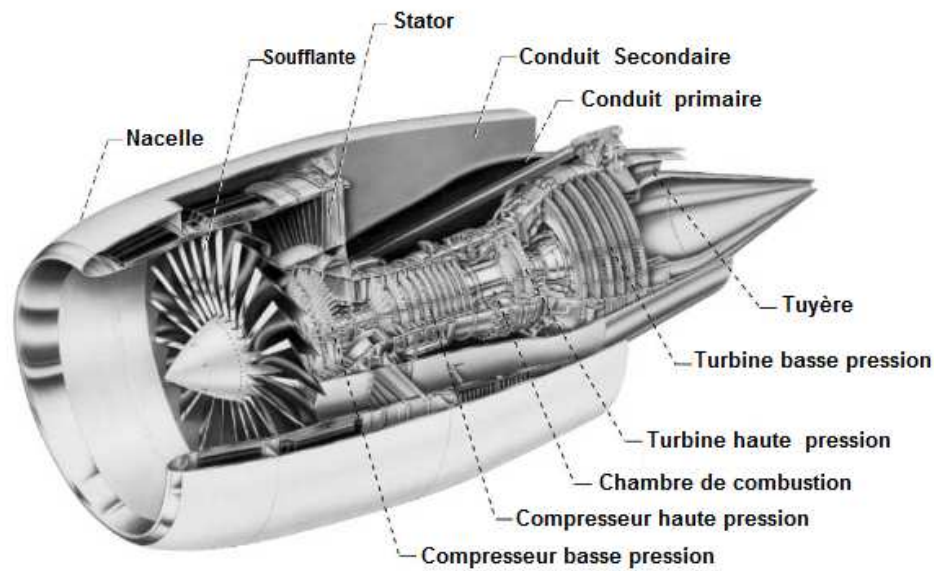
Vue en coupe d'un turboréacteur [83]
